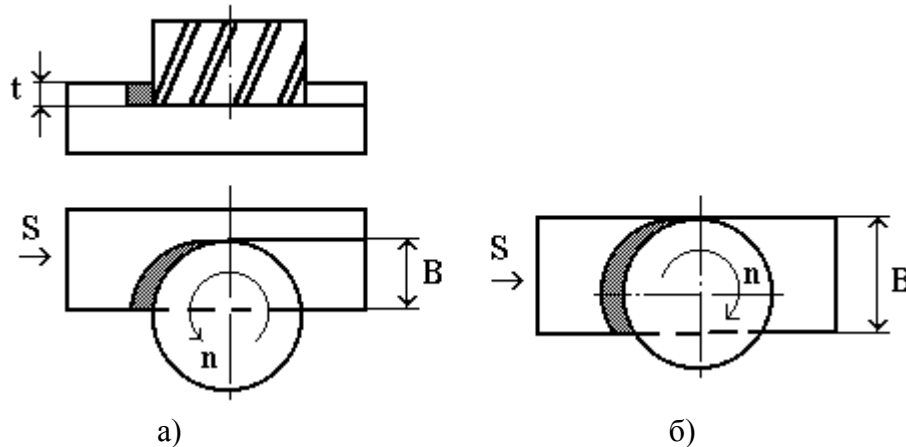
Схема фрезерования торцевой фрезой преимущественно:
